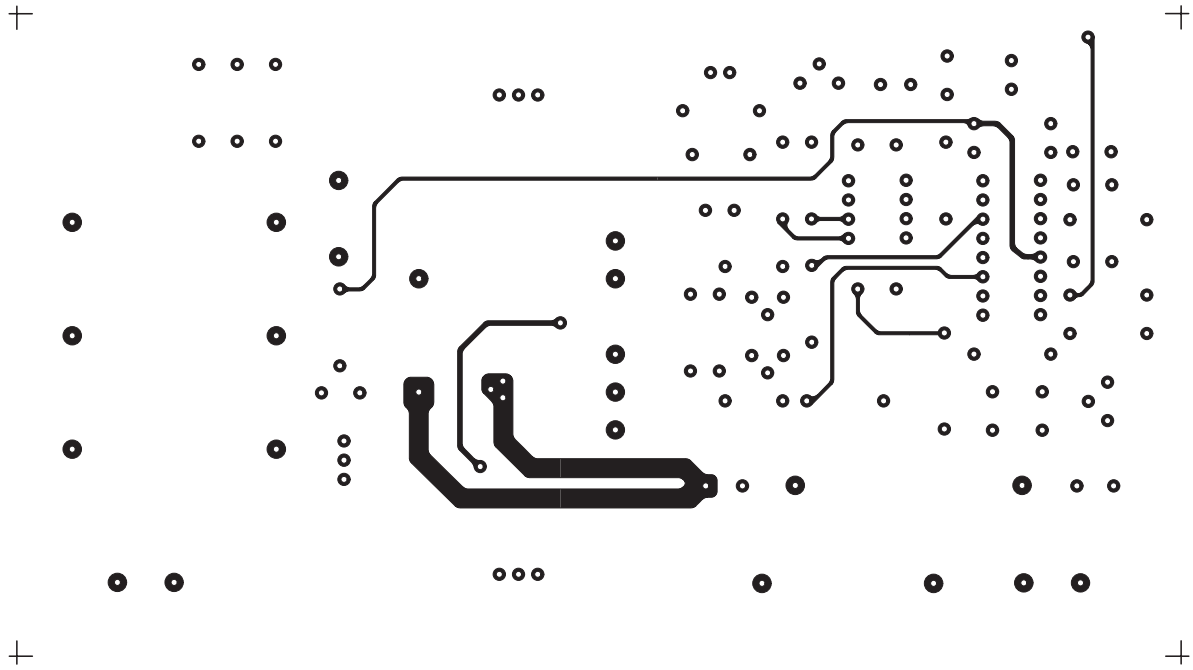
2 : Dessin, à l'échelle 1, du circuit imprimé double face à trous métallisés du générateur EN1759, côté composants.
